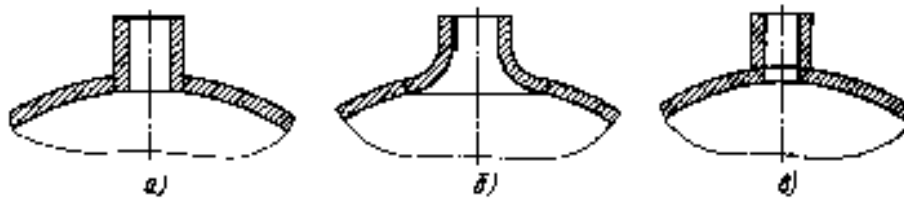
Конструкції зварного з'єднання штуцера з обичайкою
